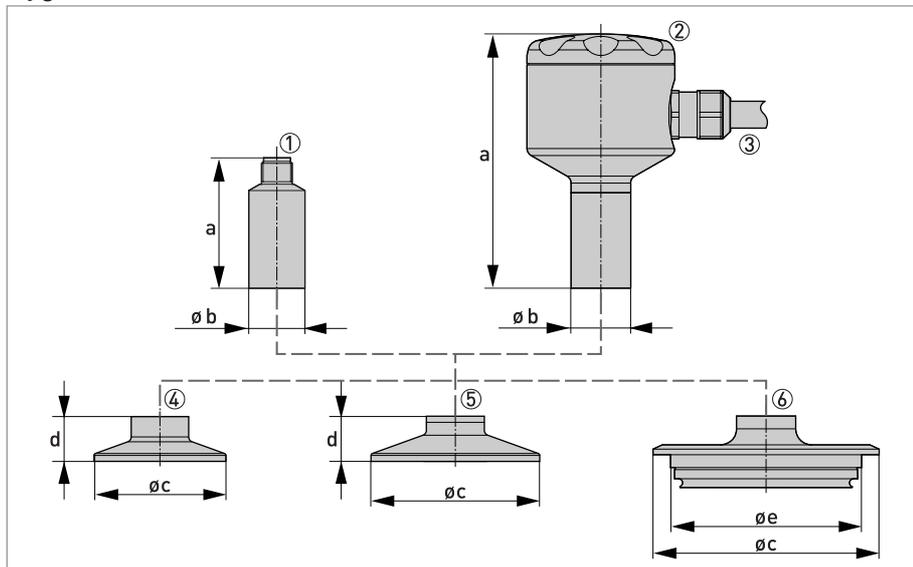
Abmessungen für Drucktransmitter mit hygienischen Anschlüssen
